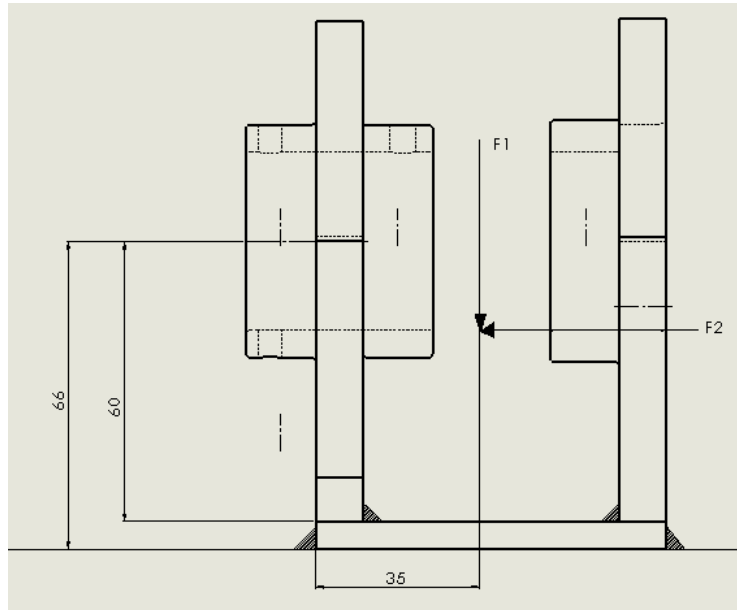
Vista frontal de los cordones de soldadura.
